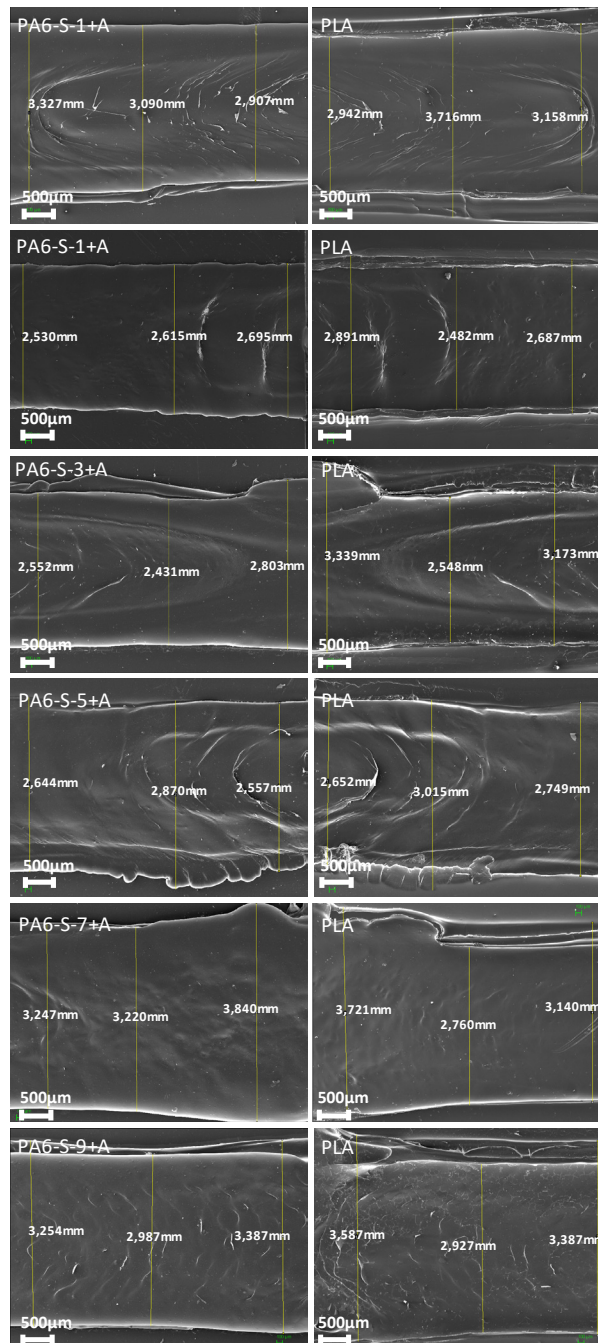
Determinación del cordón de soldadura de las soldaduras de los sistemas PLA/PA6 ensayados a despegado.
